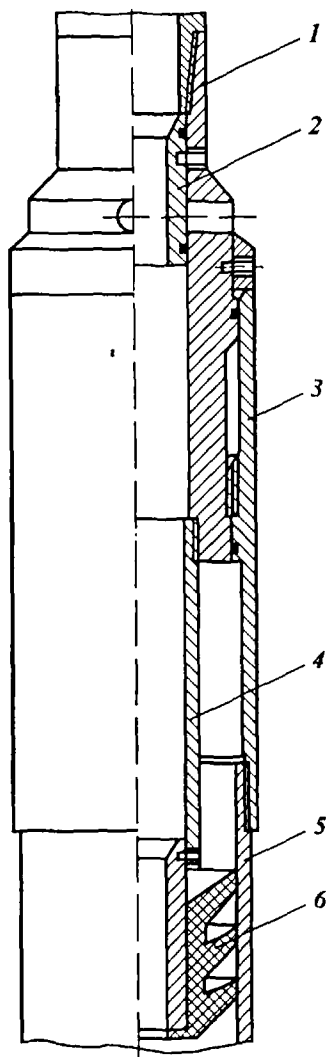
Разъединитель резьбовой колонн типа РРС
